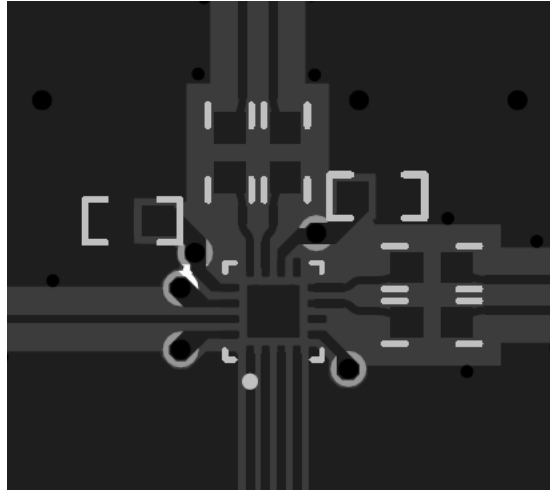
LMK3H0102 的 PCB 布局示例，顶层
